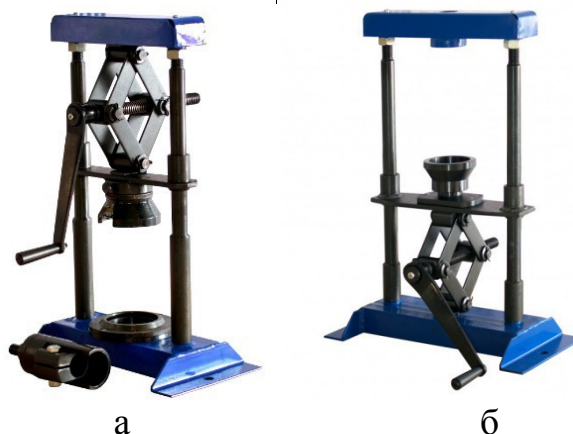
Стенды С1 (а) и С2 (б) для разборки и сборки энергоаккумулятора тормозной камеры автомобиля КамАЗ
